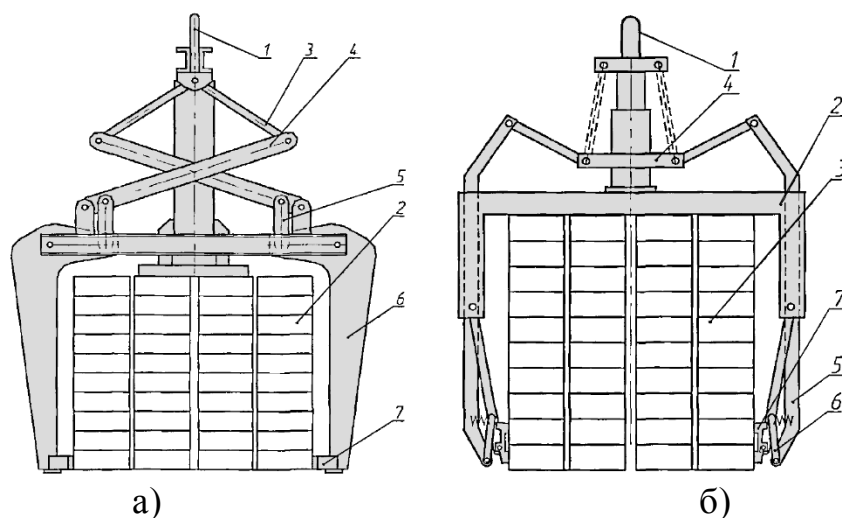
а) зажимной захват с неповоротными прижимами и б) грузозахватное устройство с поворотными прижимами
